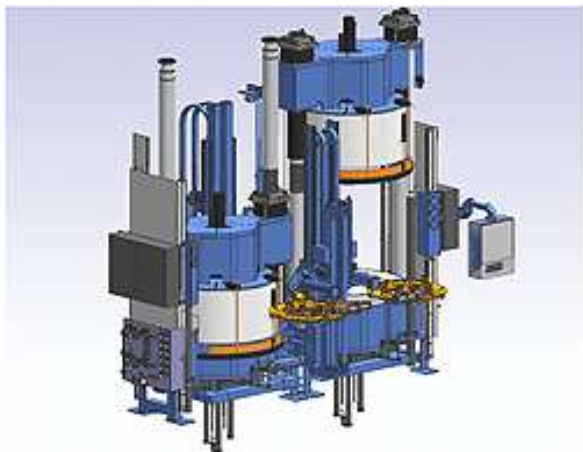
Sloupový typ LT-XW 52" [14]
